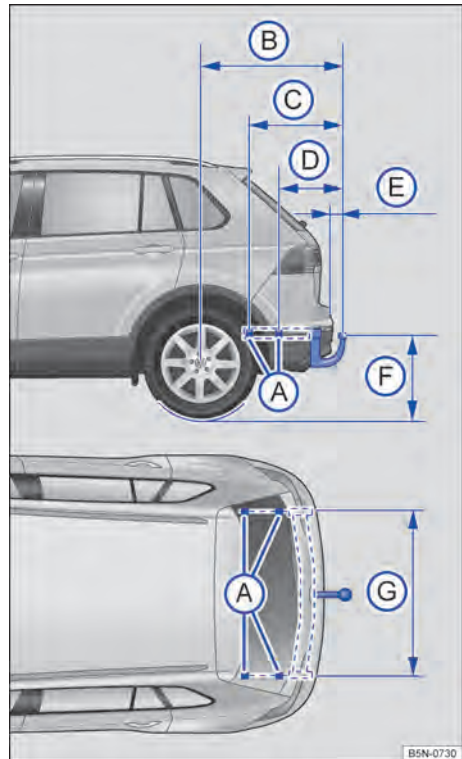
Dimensões e pontos de fixação para instalar um dispositivo de reboque posteriormente.
